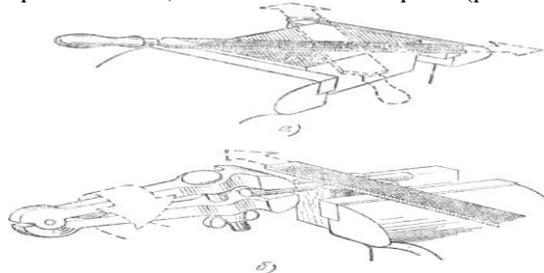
Опиливание поверхностей: а — широкой плоской, б — цилиндрической
